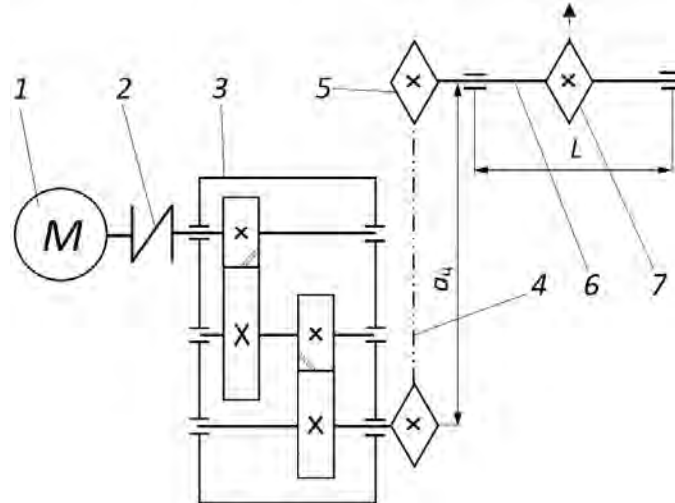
Схема привода скребкового конвейера (вид сверху): 1 – асинхронный электродвигатель; 2 – муфта упругая с резиновой звездочкой; 3 – редуктор двухступенчатый (с цилиндрическими косозубыми передачами); 4 – цепная передача; 5 – звездочка цепной передачи с предохранительным устройством; 6 – приводной вал; 7 – приводная звездочка
